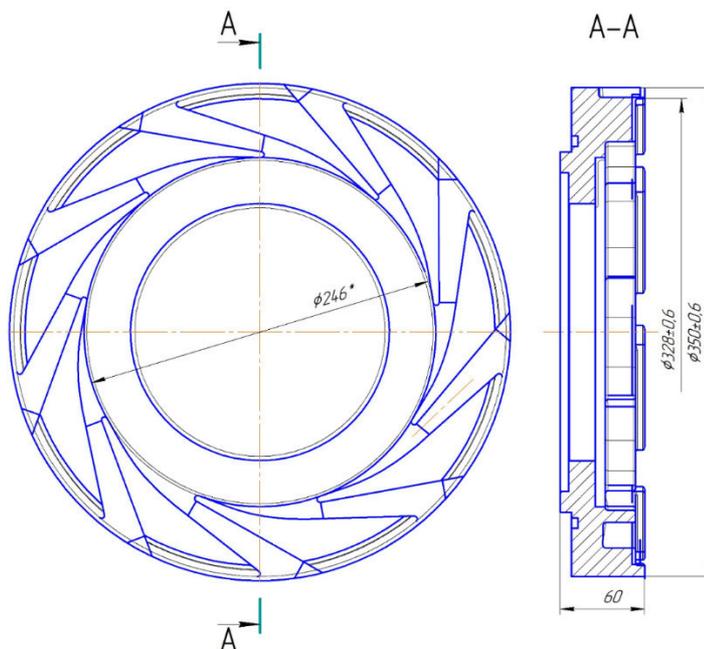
Эскиз детали «Аппарат направляющий»
